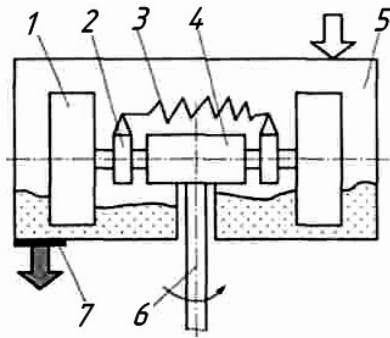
Катковый смеситель с неподвижной чашей: 1 – каток; 2 – подвеска; 3 – пружина; 4 – траверса; 5 – чаша; 6 – приводной вал; 7 – разгрузочный люк
